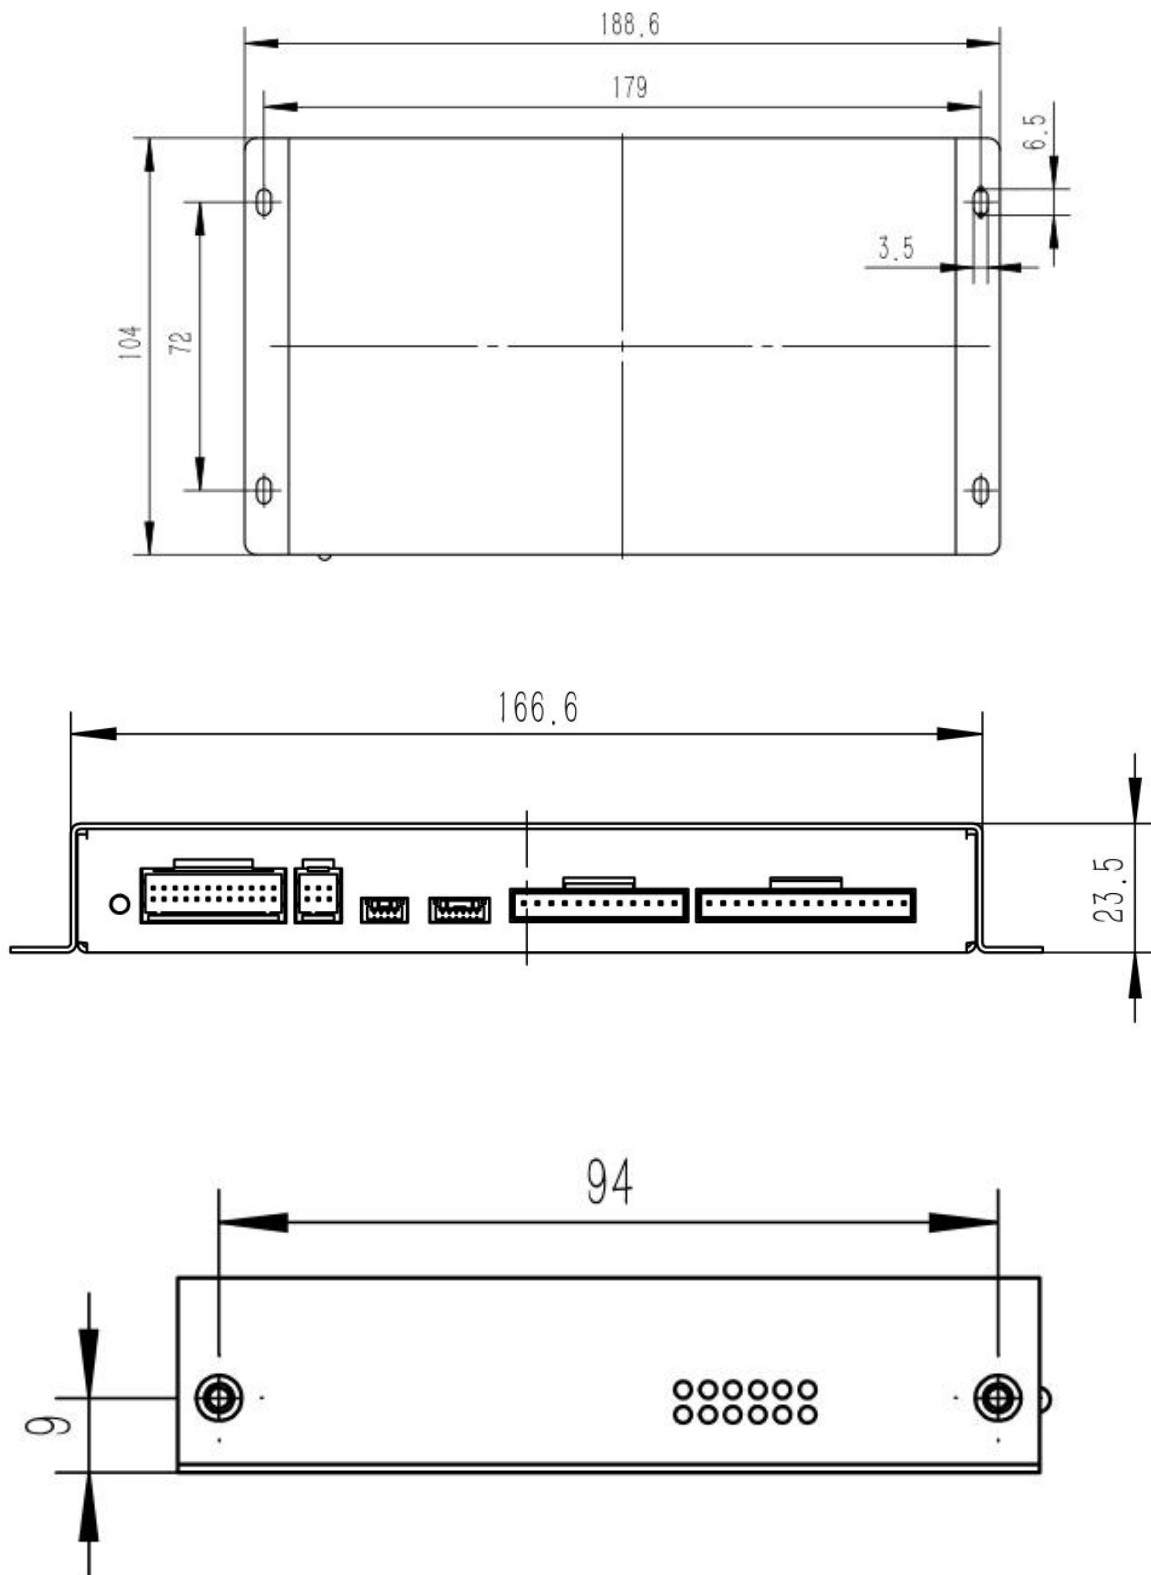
JK-B2A25S-RP 外形尺寸图 Fig. 3 outline dimension of JK-B2A25S-RP
